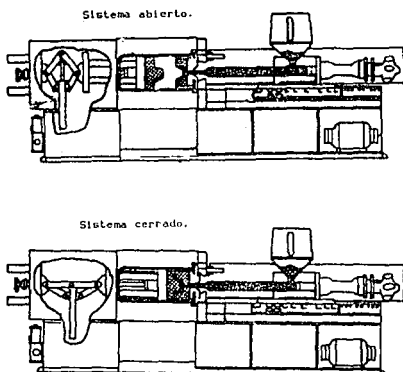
Sistema de cierre de una máquina de inyección [4].
